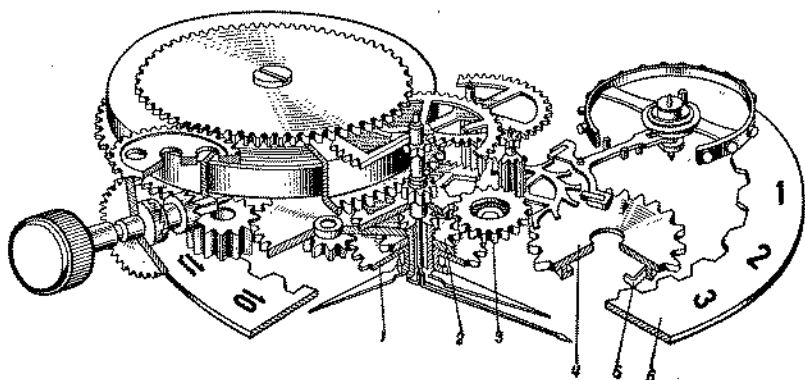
Кинематическая схема календарного устройства часов «Полет» 2414;
